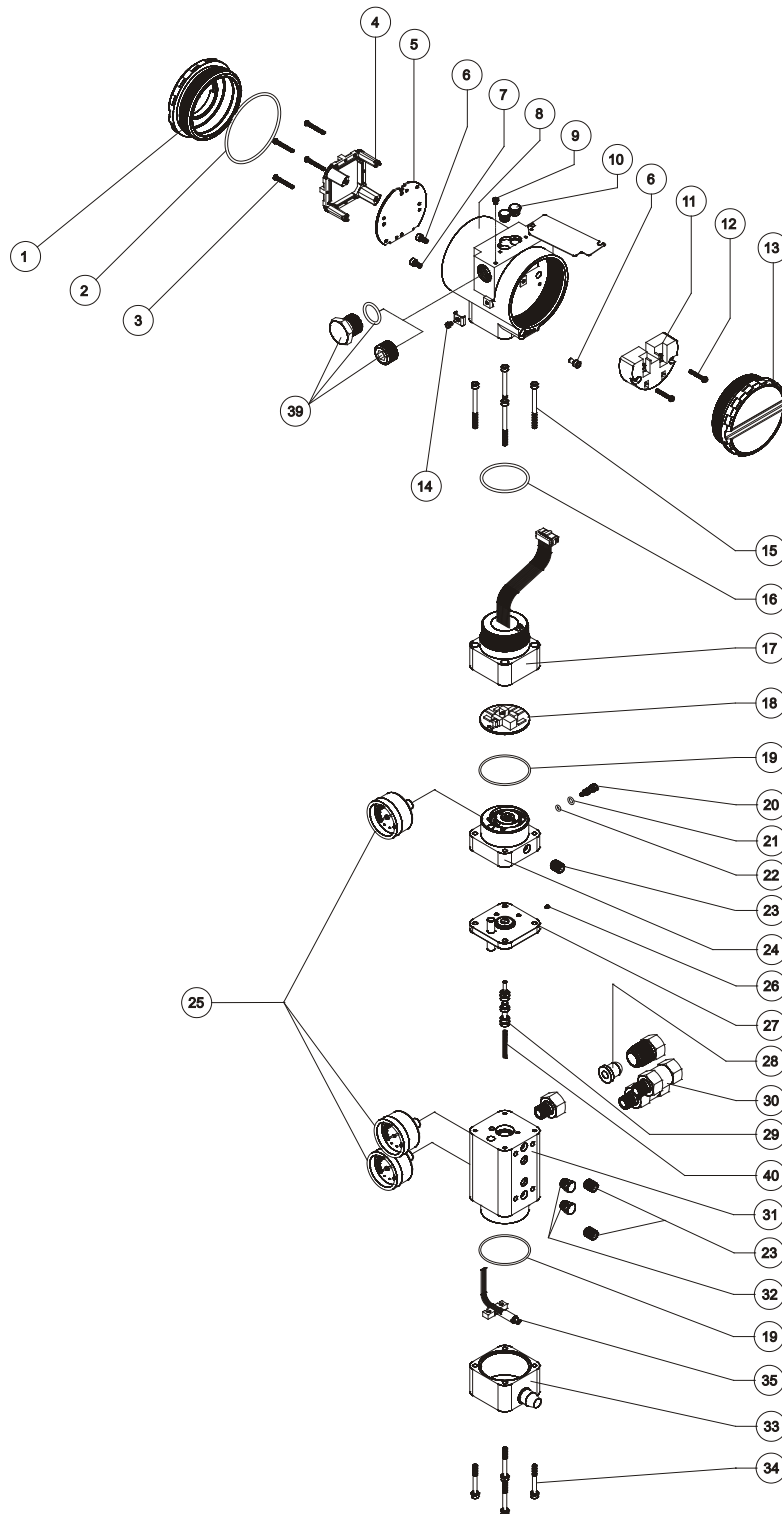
Vista Explodida do Posicionador FY303 do ACP
